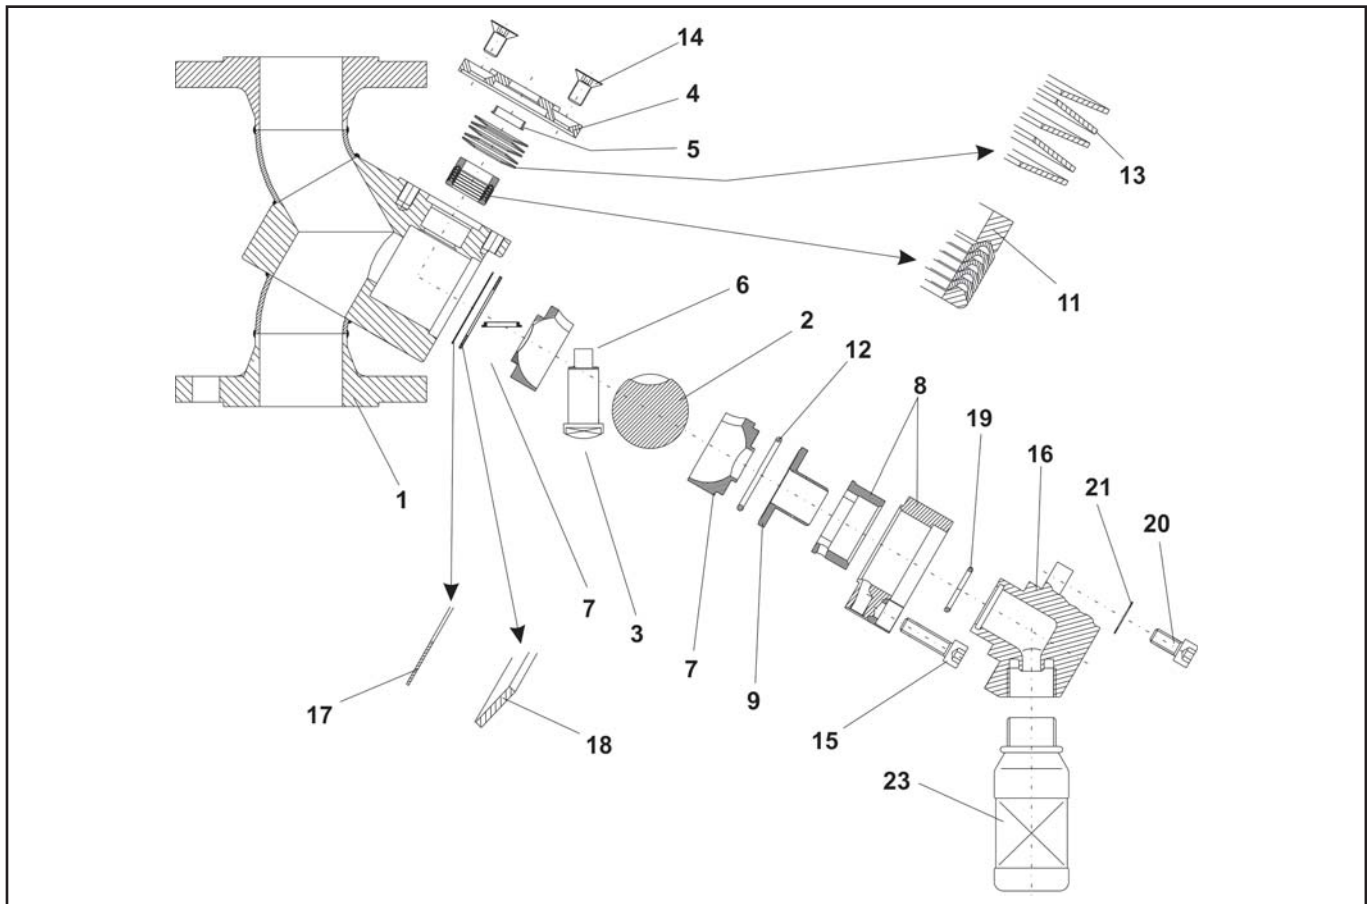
Explosionszeichnung des Probenehmerhahns BR 27g
